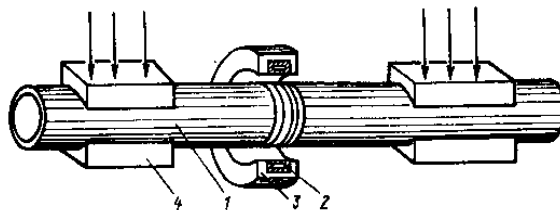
Схема стыковой высокочастотной сварки труб:
